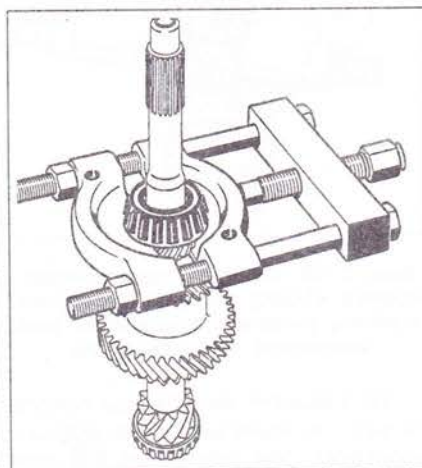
Извлеките подшипники прессом при помощи съемника.
